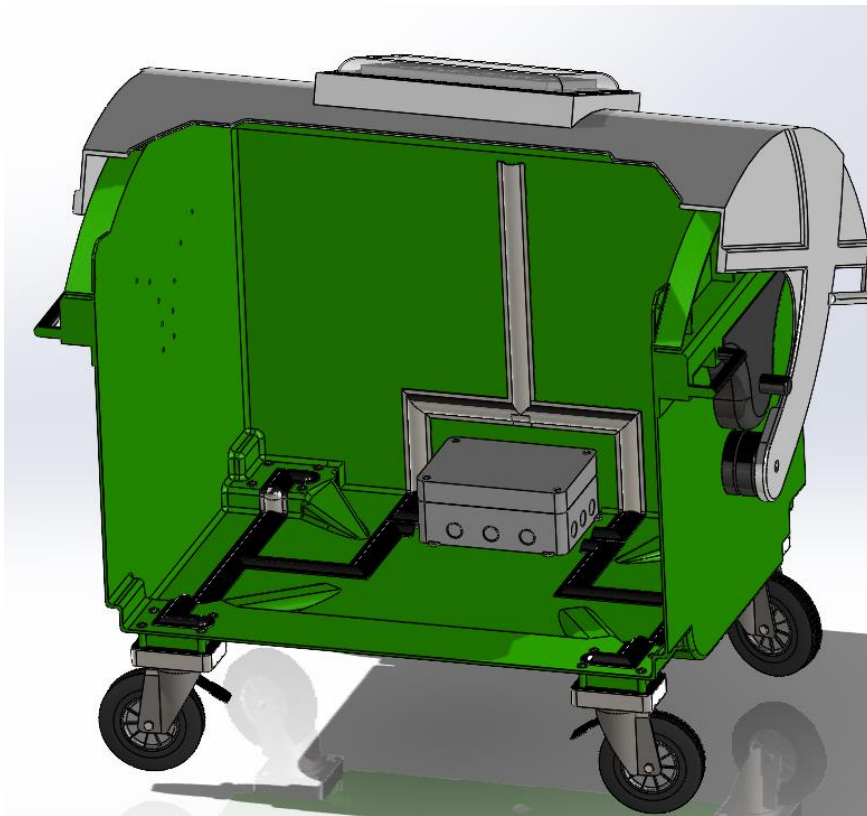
Modelação em ambiente SolidWorks – Montagem final - Vista isométrica em corte
